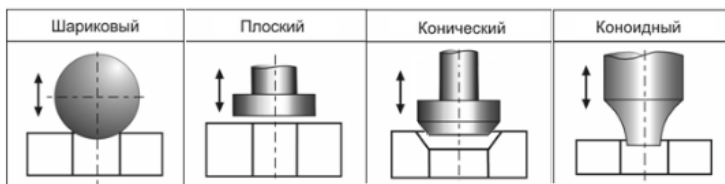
Гидроклапаны с различными запорно-регулирующими элементами
